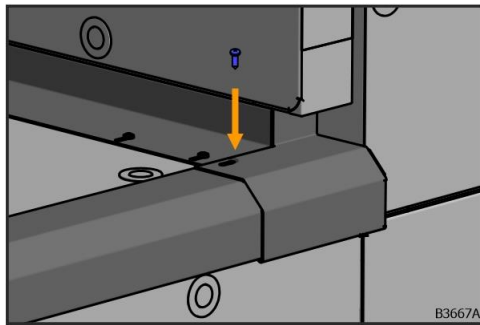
Montage de l'extrémité de la cornière casse-goutte
